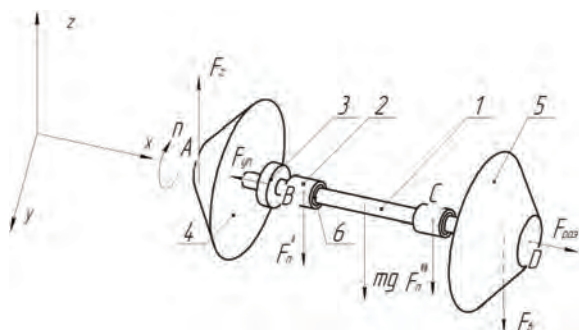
Схема ротора турбокомпрессора с подшипниками
